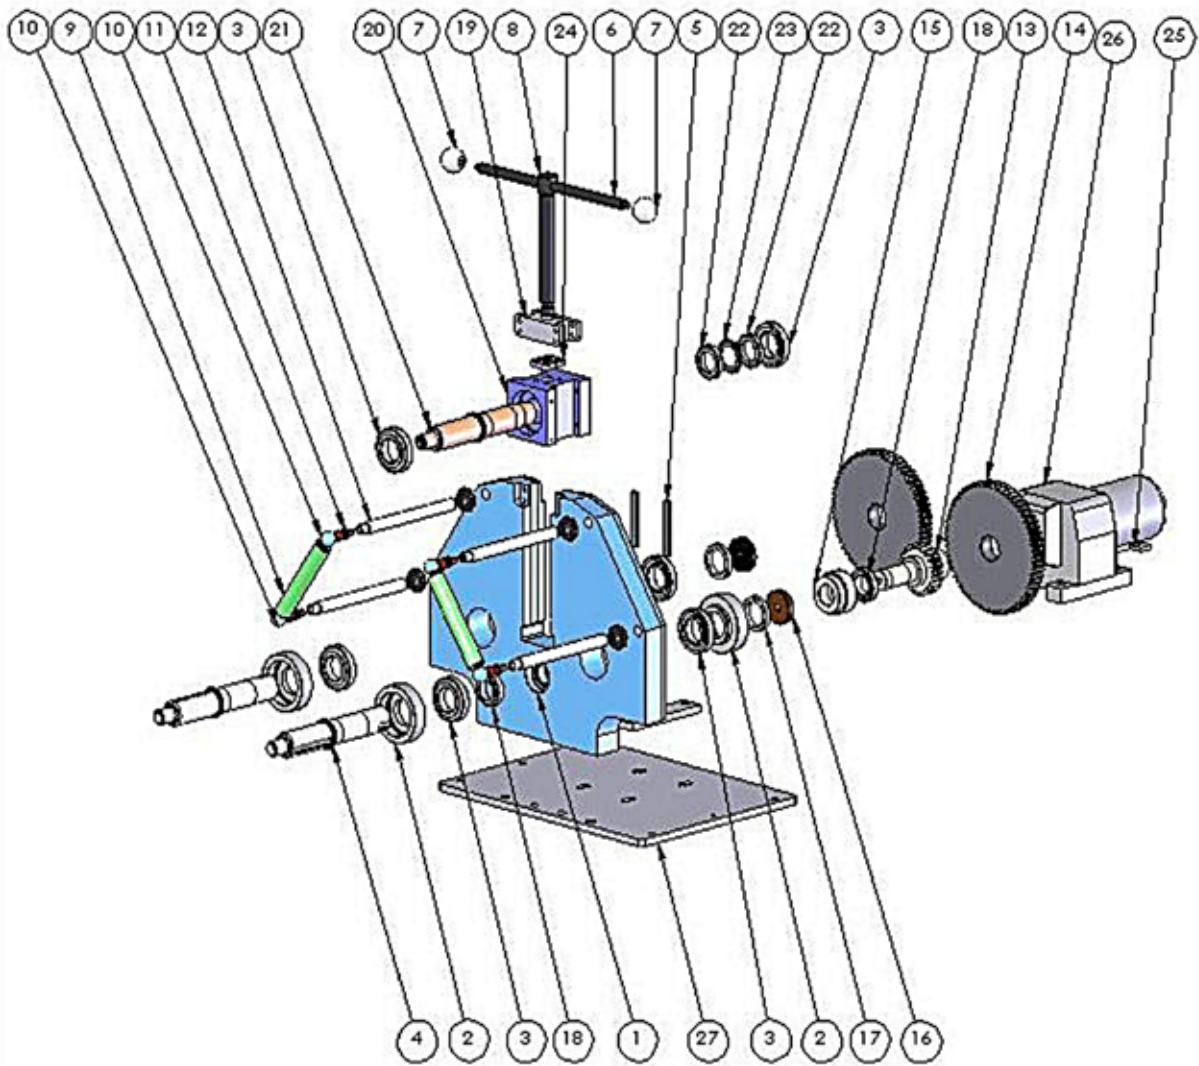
Opengewerkte tekening 2 - PRM 30 F
